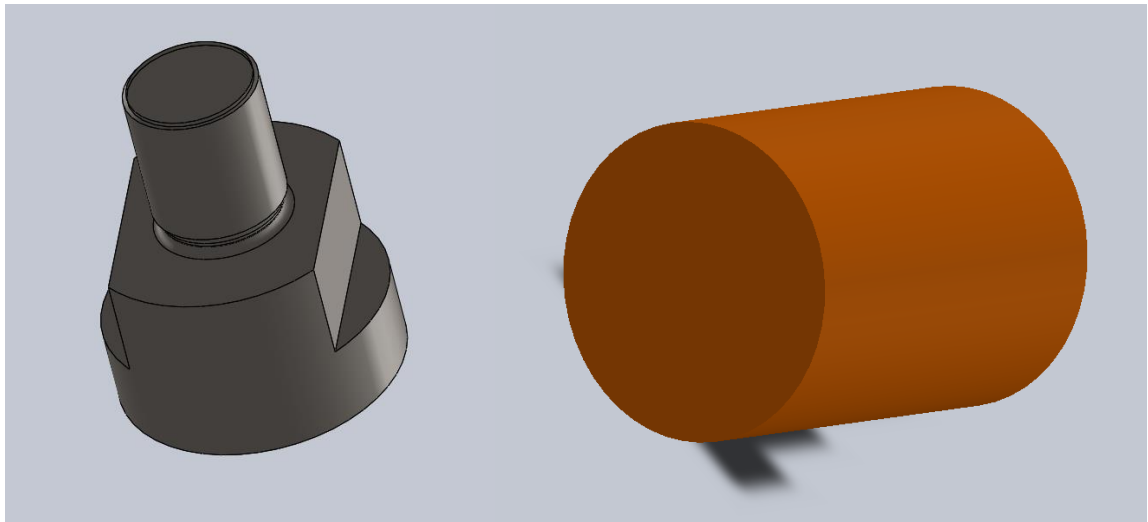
3D модель заготовки та деталі «П'ята» (Заготовка – 3,54 кг)
